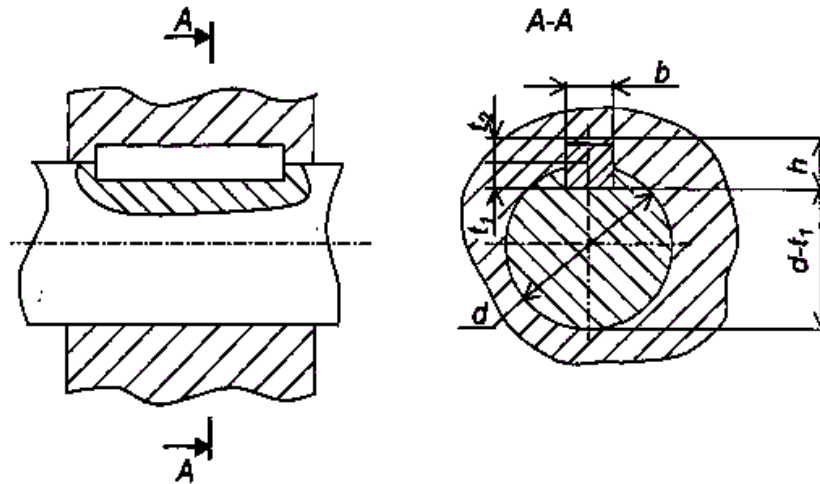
Схема шпоночного з'єднання валу з робочим колесом.
